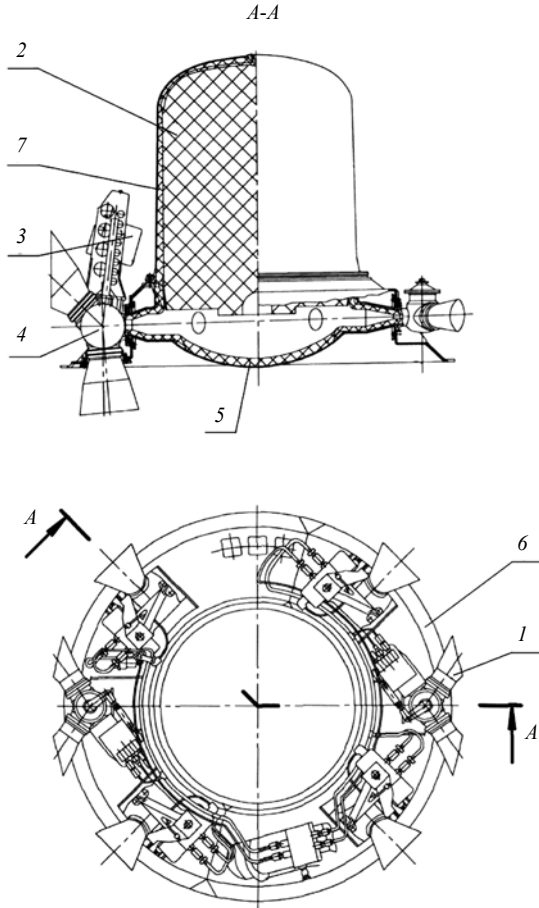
Конструктивная схема регулируемого двигателя: 1 – сопловой блок крена; 2 – топливный заряд; 3 – рулевая машина; 4 – сопловой блок тангажа и рыскания; 5 – сопловая крышка; 6 – агрегатный отсек; 7 – камера сгорания
